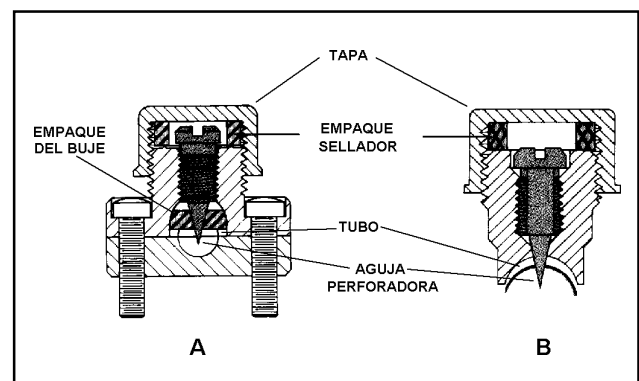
Válvulas perforadoras típicas. (A) atornillada, (B) soldable.
